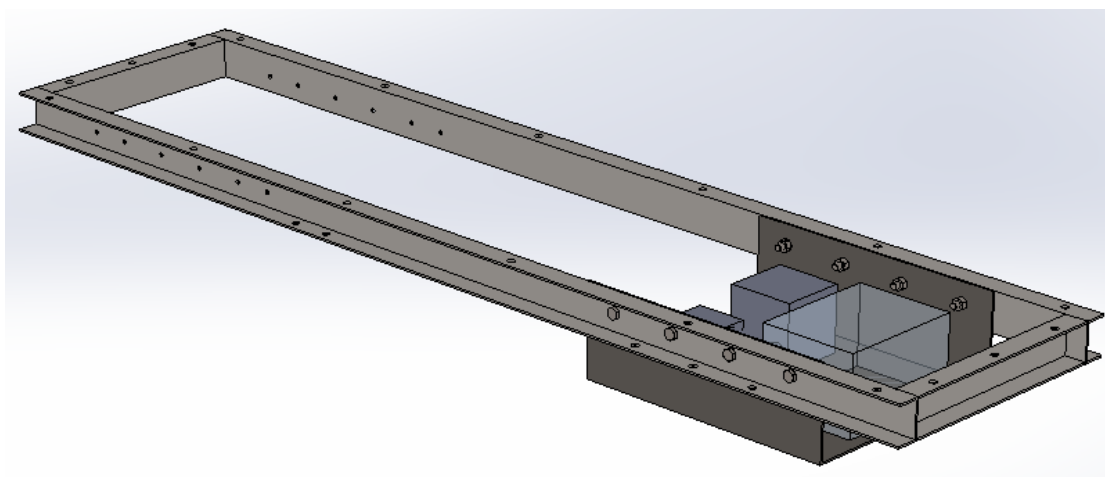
Montagem da caixa de suporte na estrutura retangular
